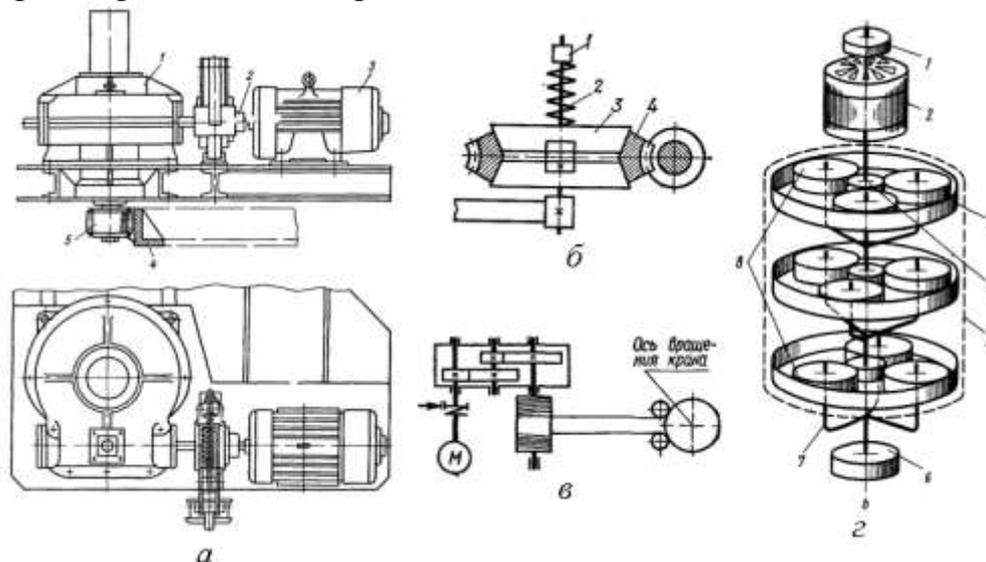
Кинематические схемы механизмов поворота кранов: а – с червячным редуктором; б – предохранительная муфта к червячному редуктору; в – канатный привод; г – привод с планетарным редуктором.
